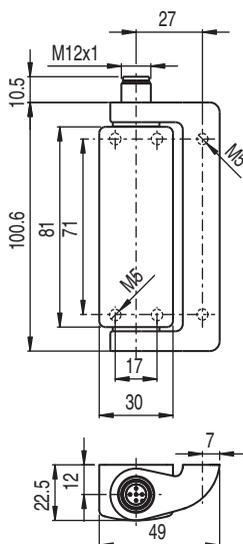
Dimensões do S400-M4M12-T em mm
